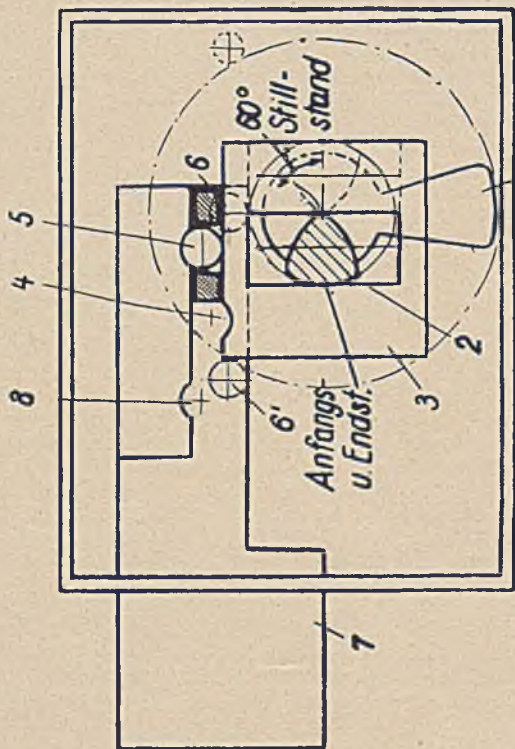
Schließwerk mit gesteuerter Kugelverriegelung durch Bogendreieckgetriebe
